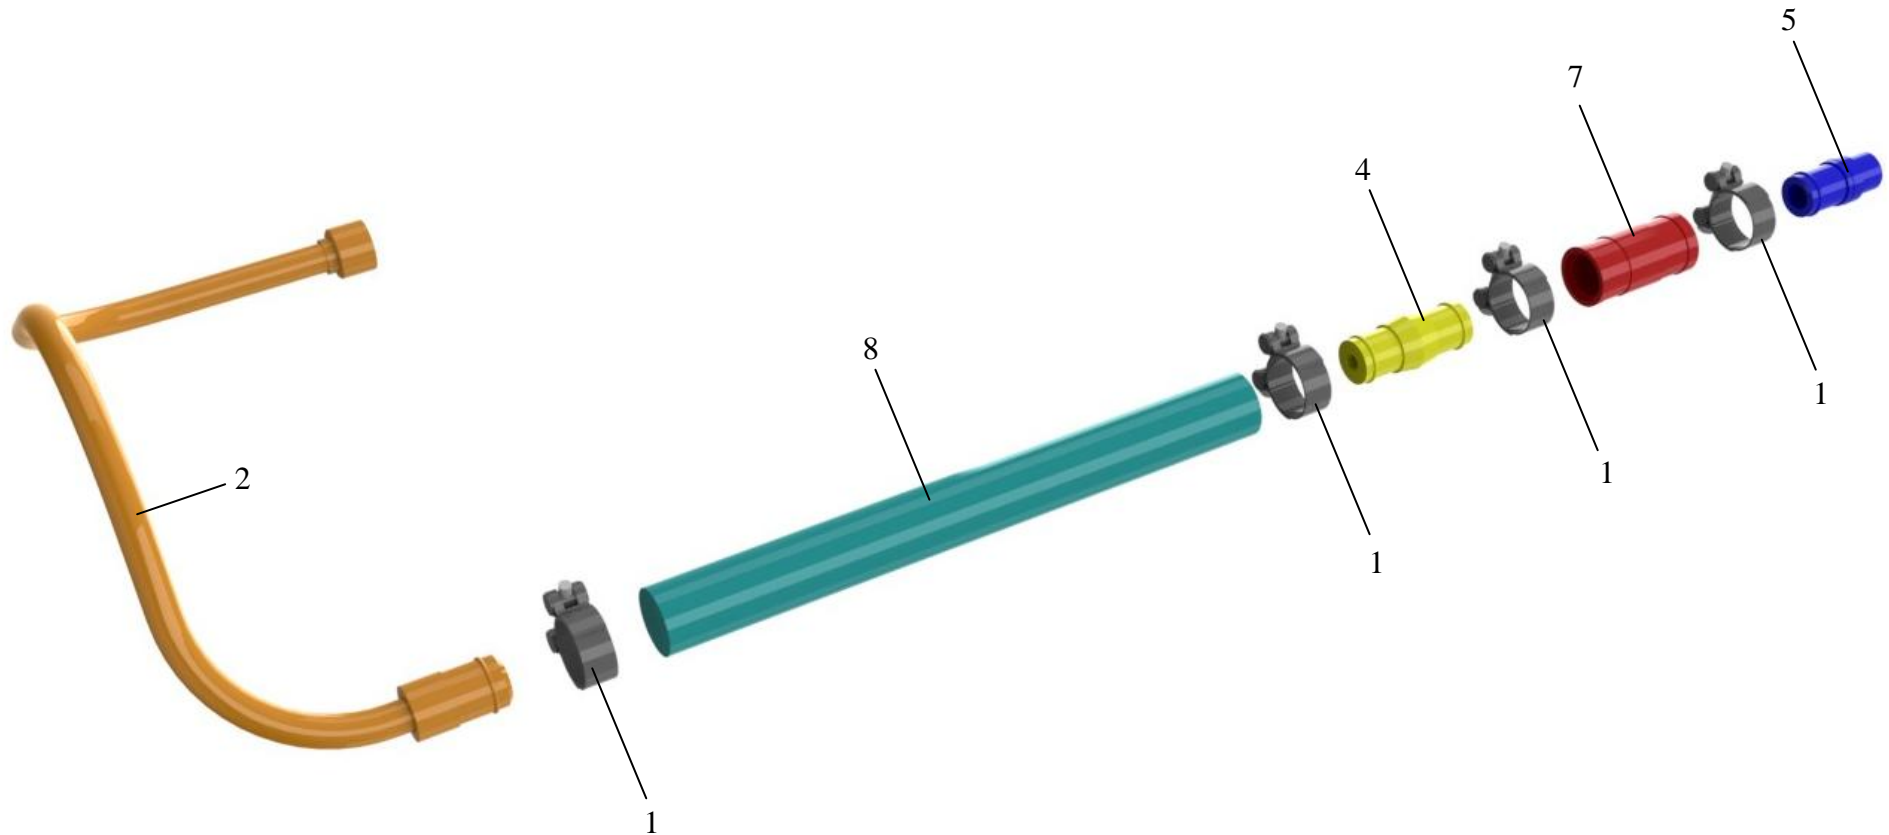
Труба компрессора АКСМ 32102-230303.000-10
